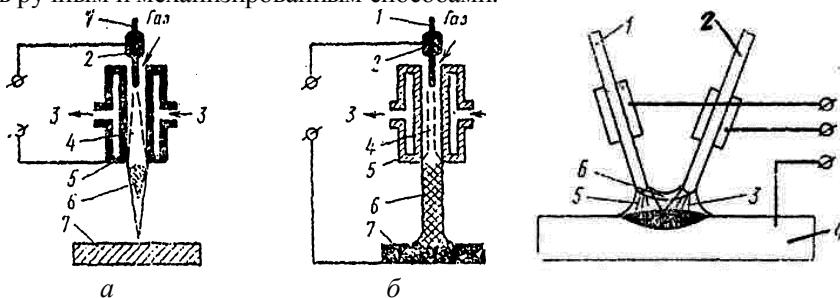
Плазменная сварка: а – плазмой, выделенной из столба дуги; б – плазмой, совпадающей со столбом дуги; 1 – вольфрамовый электрод; 2 – токоподводящий мундштук; 3 – охлаждающая вода; 4 – столб дуги; 5 – медное сопло; 6 – плазма; 7 – основной металл
